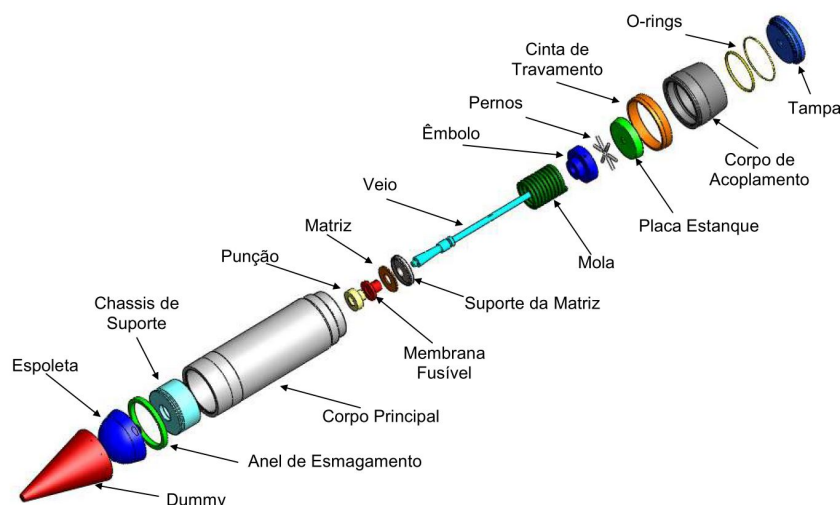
Conjunto de componentes que constituem o FIREND 105 mm [2].
